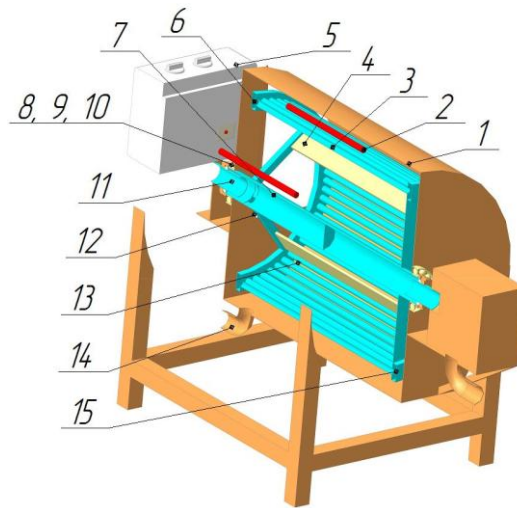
СВЧ установка для массажирования и термообработки кускового мясного сырья: 1 – цилиндрический экранирующий корпус; 2 – ИК лампы; 3 – трубчатая резонаторная камера; 4 – лопасти; 5 – генераторный блок с магнетроном и излучателем; 6 – кольцевая труба; 7 – полый вал; 8 – подшипниковый узел; 9 – диэлектрическая прокладка; 10 – стопорная гайка; 11 – муфта; 12 – люк; 13 – щель между трубами; 14 – сливной патрубков, 15 – полый диск
